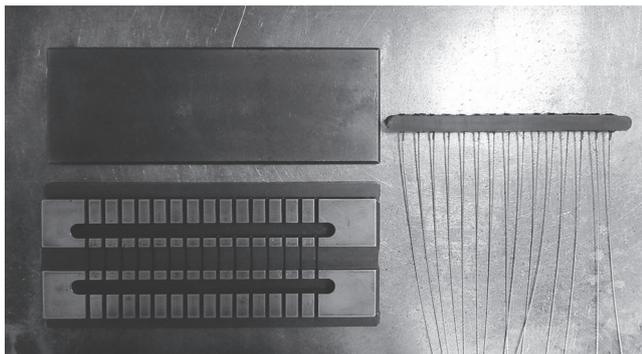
Пресс-форма и готовый резинокордный блок метода ASTM D 2229
